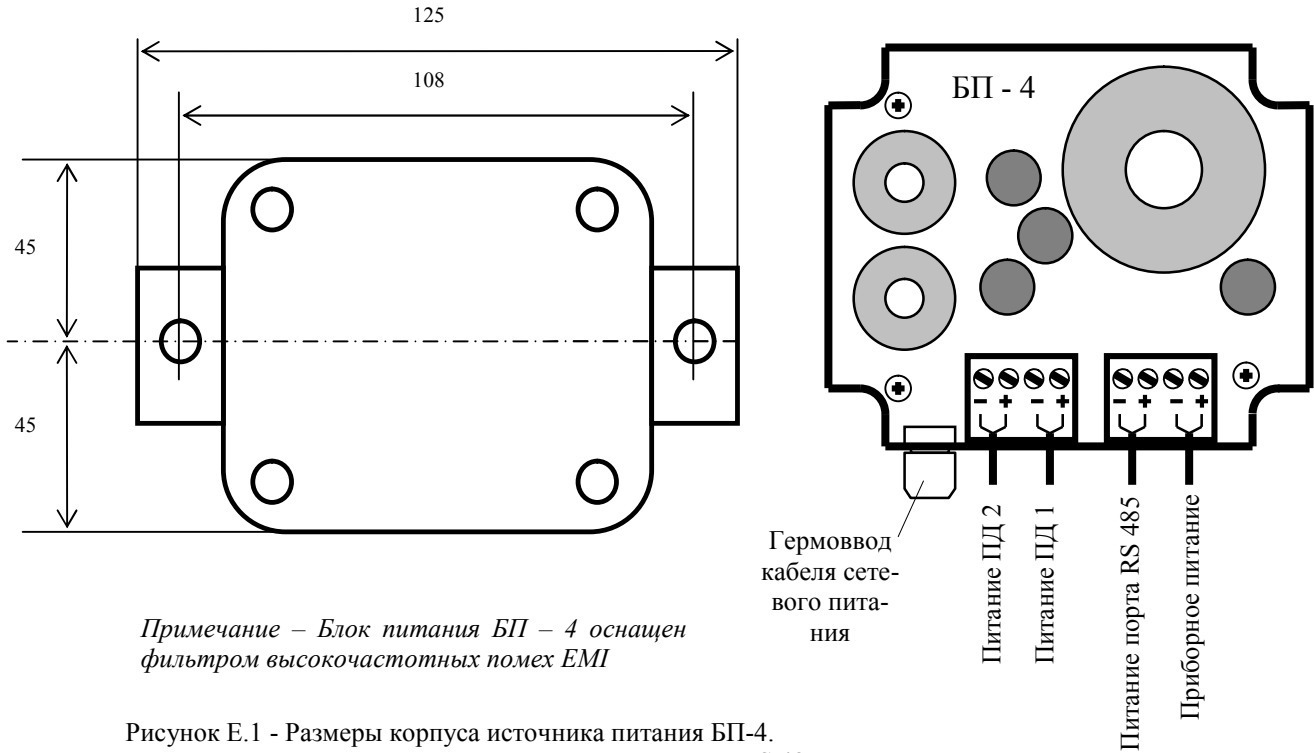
Размеры корпуса источника питания БП-4.
